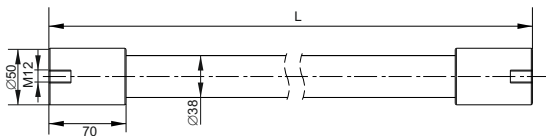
Габаритные размеры штанги / Figure 1 – Overall dimensions of the bar /
